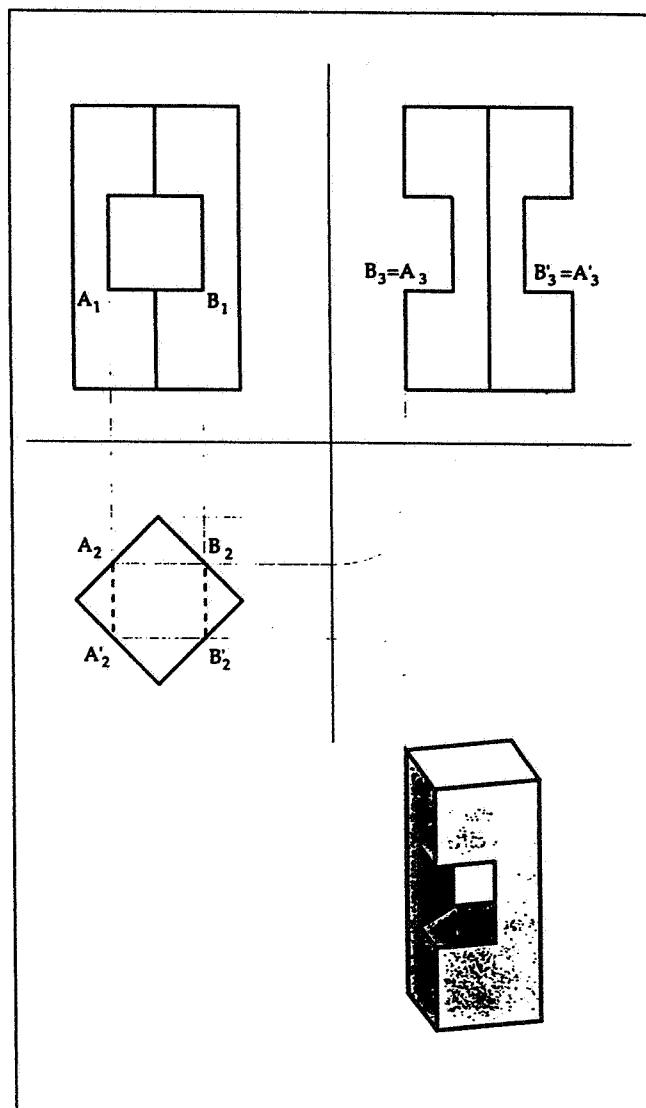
Intersezione di un prisma retto con un foro prismatico.
